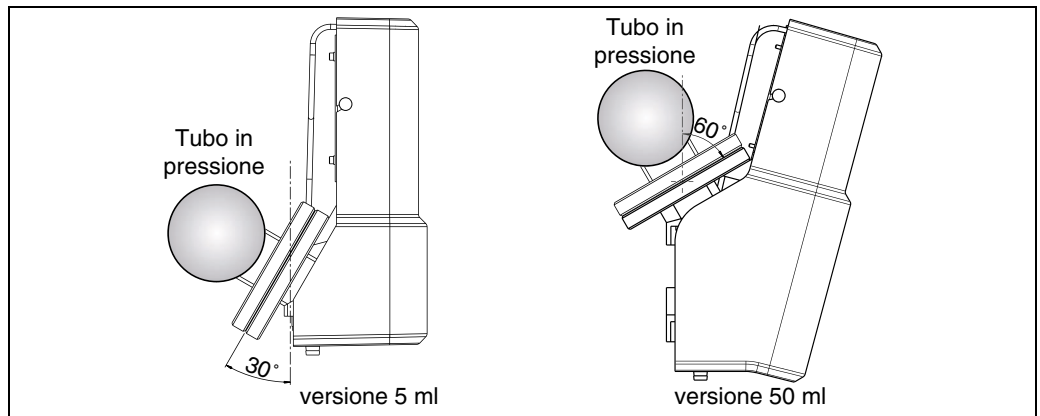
Posizione di installazione dell'armatura ASP Inline
